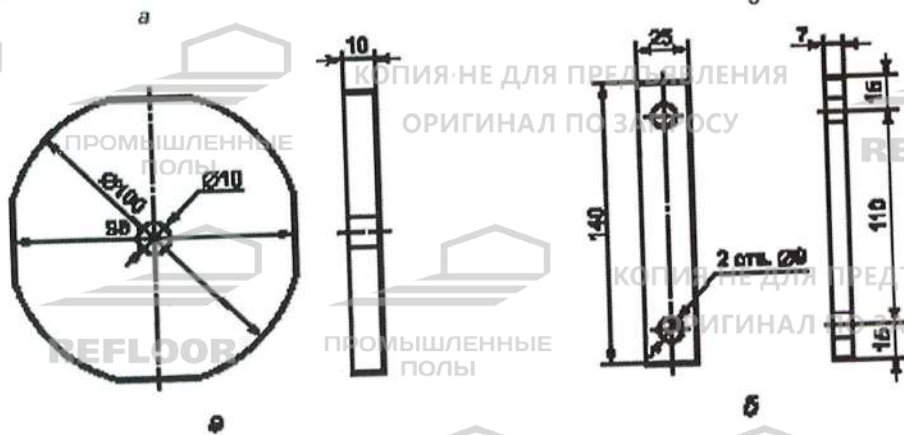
Общий вид образцов для испытаний: а – вращающийся диск, б – пластина
